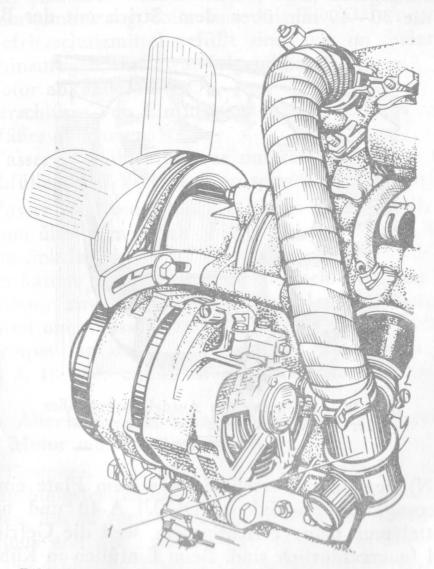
Anordnung des Thermostats am Motor: I — Thermostat
